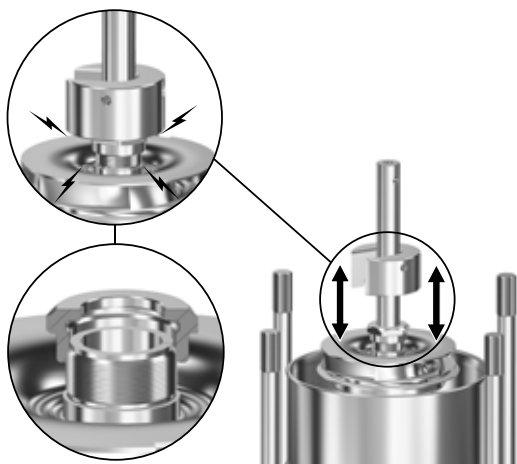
Снятие рабочего колеса (49 или 49а) с помощью приспособления С
